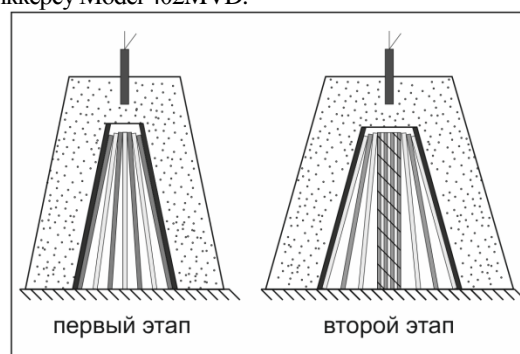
Схема сварки металлического слоистого композиционного материала за два этапа
